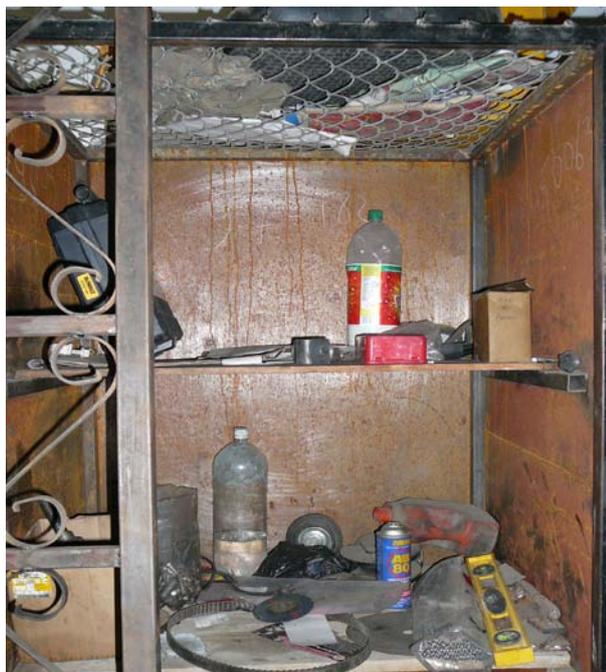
Herramientas en la sección de soldadura del DMVIML. Fuente: Autor.
